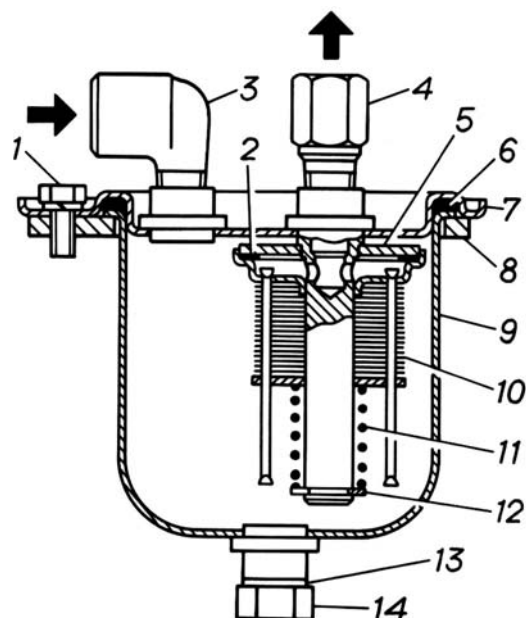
Топливный фильтр-отстойник: 1 - болт крышки; 2 - прокладка фильтрующего элемента; 3 и 4 - штуцеры; 5 - шайба; 6 - прокладка крышки; 7 - крышка; 8 - кронштейн; 9 - корпус отстойника; 10 - фильтрующий элемент; 11 - пружина; 12 - шайба пружины; 13 - прокладка сливной пробки; 14 - сливная пробка
